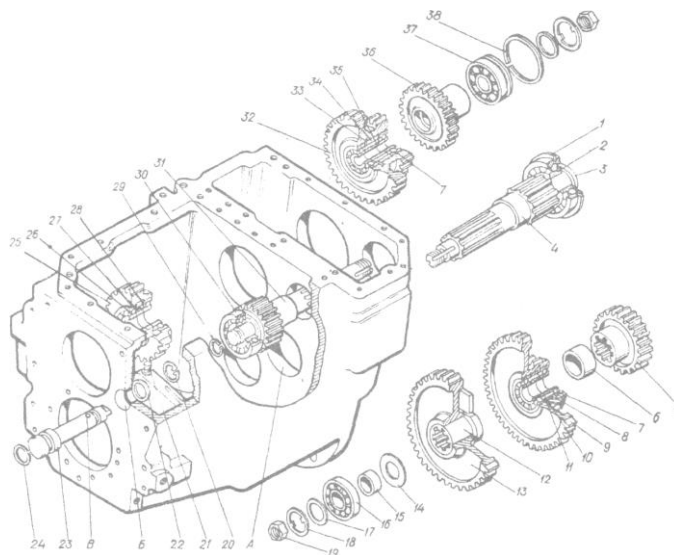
Установка зубчатых колёс и валов ходозменшувача і заднього ходу: 1, 3, 8, 20, 29, 33, 38 — кільце стопорне; 2, 7, 16, 26, 30, 37 — підшипник; 4, 31 — вал; 5, 13, 25, 36 — зубчасте колесо; 6, 10, 11, 15, 22, 34, 35 — втулка; 9, 32 — блок зубчатих колёс; 12 — муфта; 14, 24, 27, 28 — кільце; 17, 18 — шайба; 19 — гайка; 21 — болт; 23 — вісь
